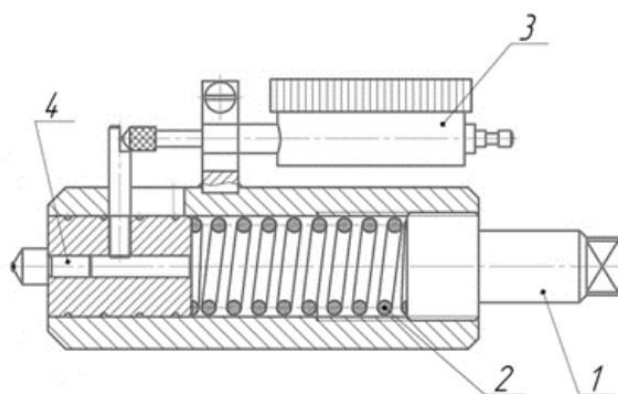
Оправка с винтовой пружиной: 1 – регулировочный винт;
